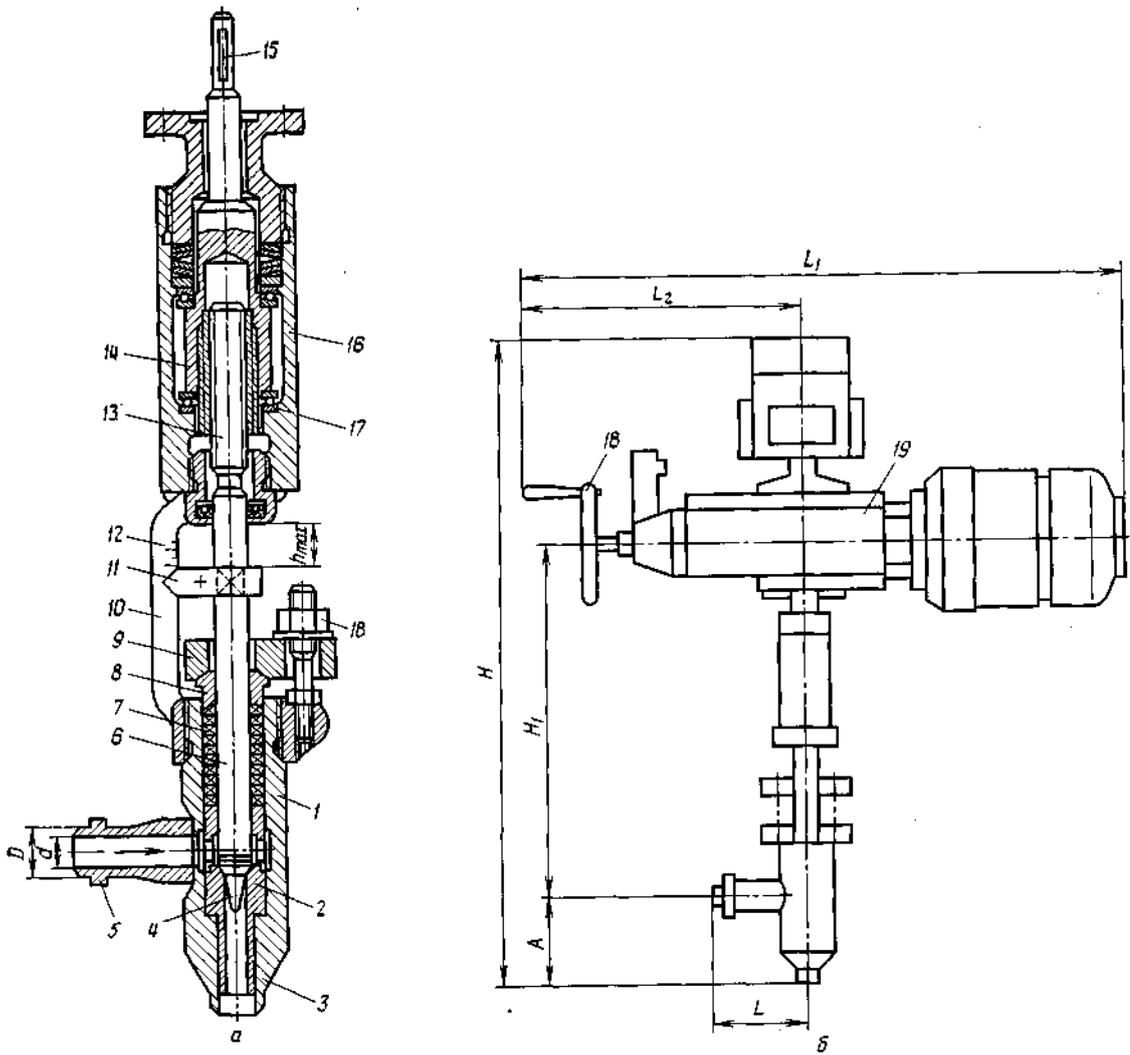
Клапан регулирующий игольчатый D_v 20, 50, 65 серий 870, 868: а — разрез; б — общий вид
